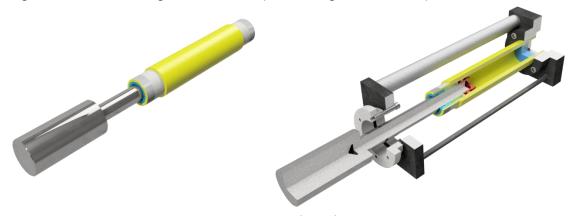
hydraulischer Zylinder (links) und konstruierter Bolzenschieber (rechts)
